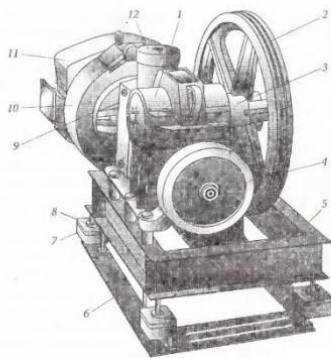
Конструкция редукторной лебедки лифтовой установки
